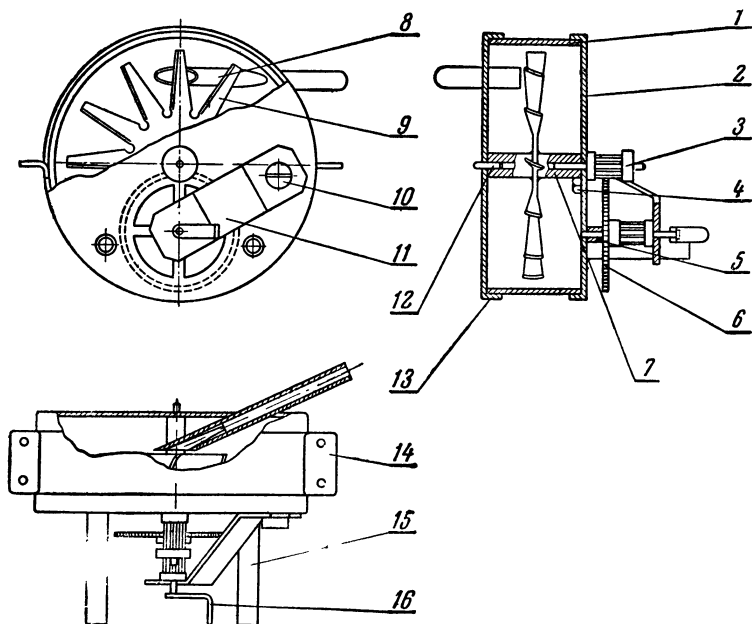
Однодисковая паровая турбина: 1 — кольцо корпуса паровой турбины; 2 — крышка корпуса; 3 — ведущая трибка; 4 — гайка; 5 — ограничительная втулка; 6 — поводковое зубчатое колесо; 7 — вал диска; 8 — сопло; 9 — диск паровой турбины; 10 — винт; 11 — кронштейн оси поводкового зубчатого колеса; 12 — ось вала диска; 13 — крышка корпуса; 14 — скобка крепления паровой турбины; 15 — паропроводные трубки; 16 — поводок
